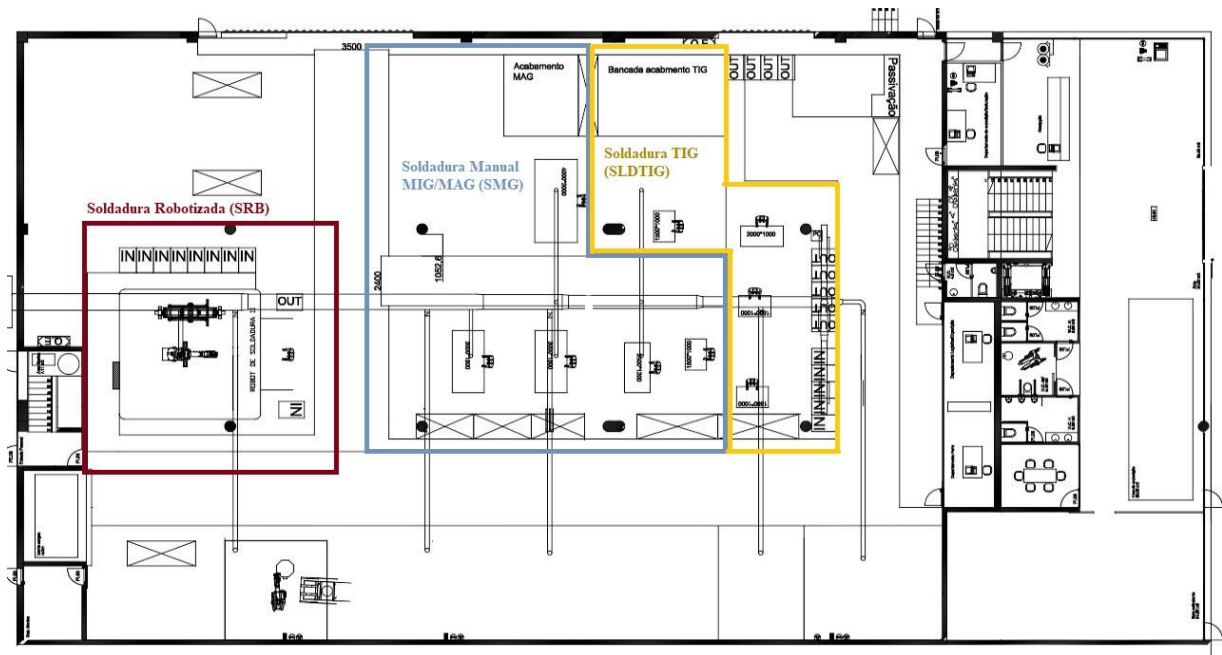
Layout* do Pavilhão Cave com os setores da soldadura
